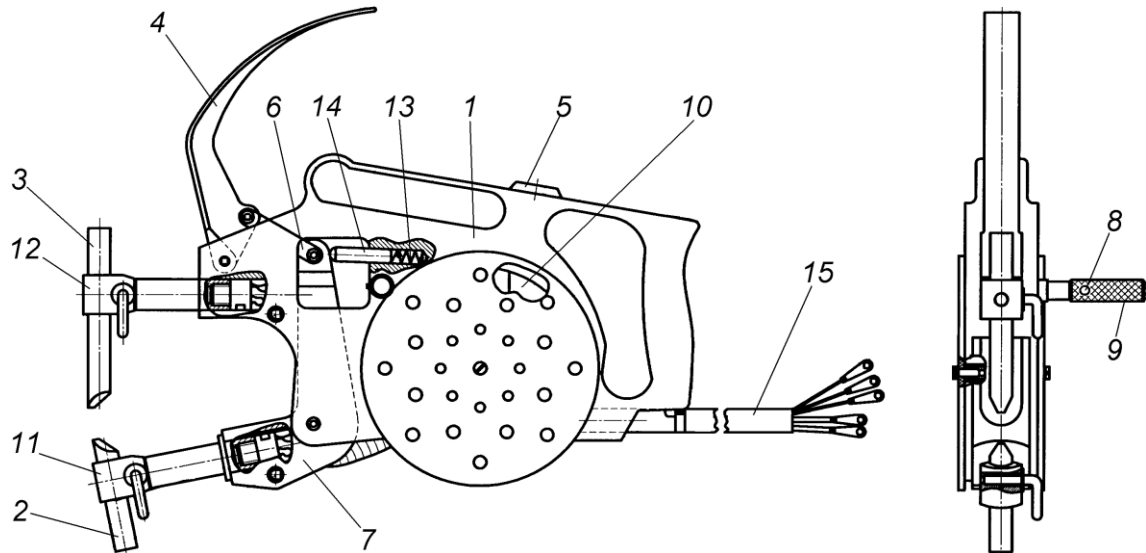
Клещи переносного ручного аппарата для контактной сварки: *1* – корпус; *15* – соединительный кабель с блоком питания (остальные обозначения в тексте)
